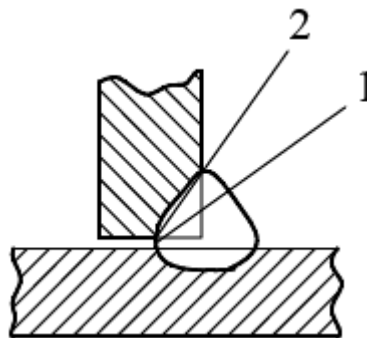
Схема расчетных сечений сварного соединения с угловым швом
